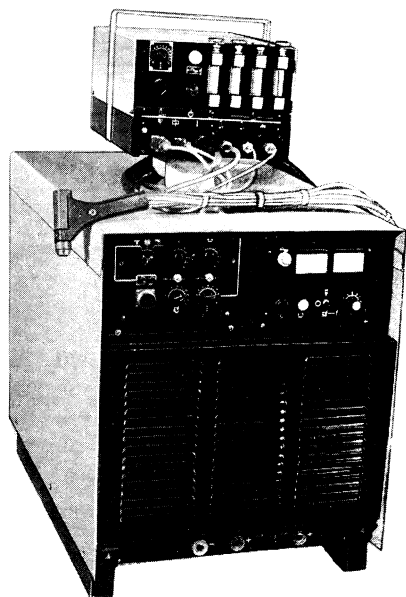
Установка для плазменной сварки УПС-301
